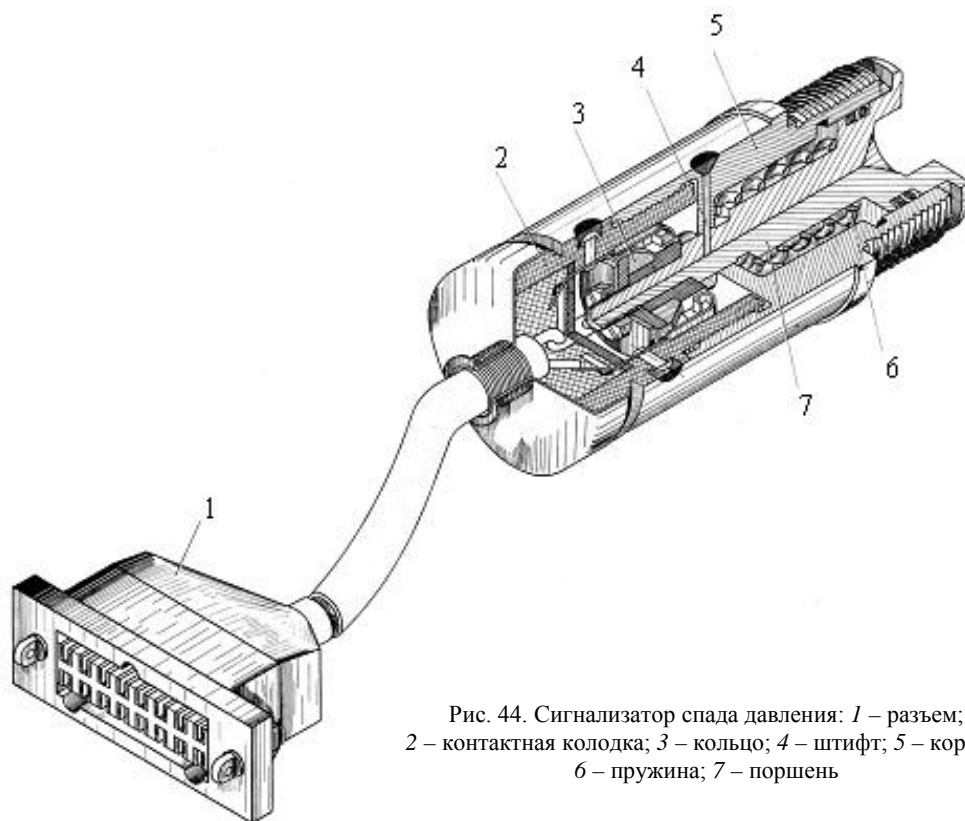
Сигнализатор спада давления: 1 – разъем; 2 – контактная колодка; 3 – кольцо; 4 – штифт; 5 – корпус; 6 – пружина; 7 – поршень
